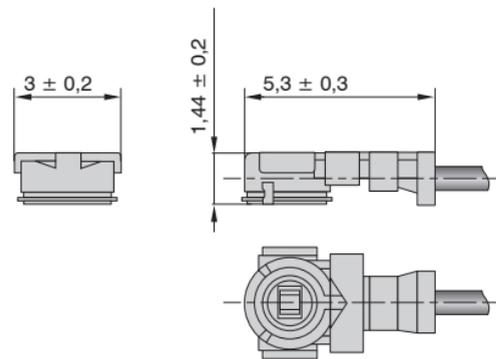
Maßzeichnung Sensorkabel, Abmessungen in mm
